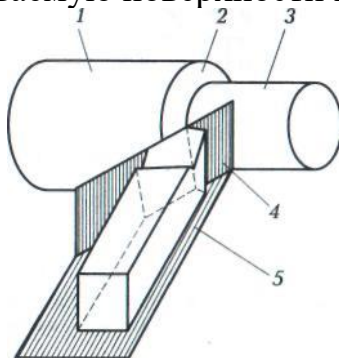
Поверхности заготовки, образуемые при обработке резцом:
